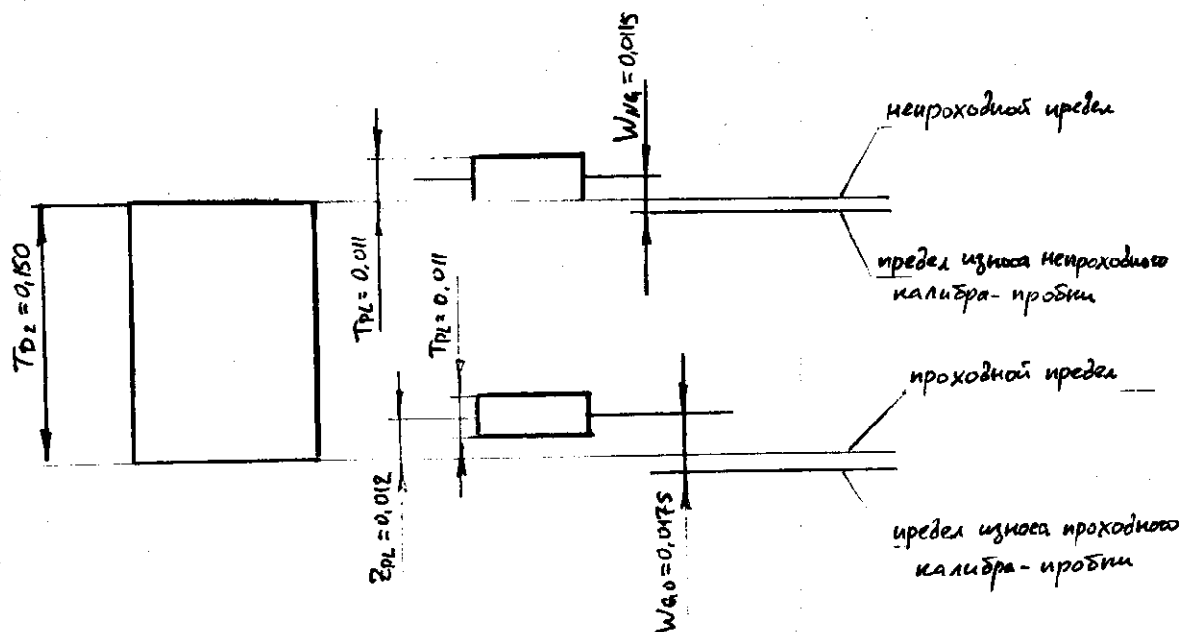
Расположение полей допусков среднего диаметра калибров для контроля внутренней резьбы
